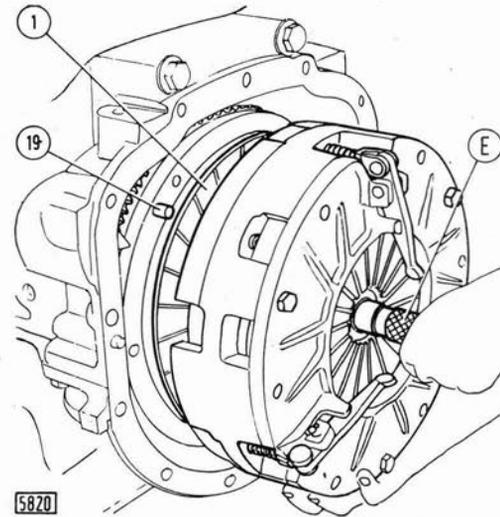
Dépose (remontage) du groupe embrayage 11" du volant moteur.
